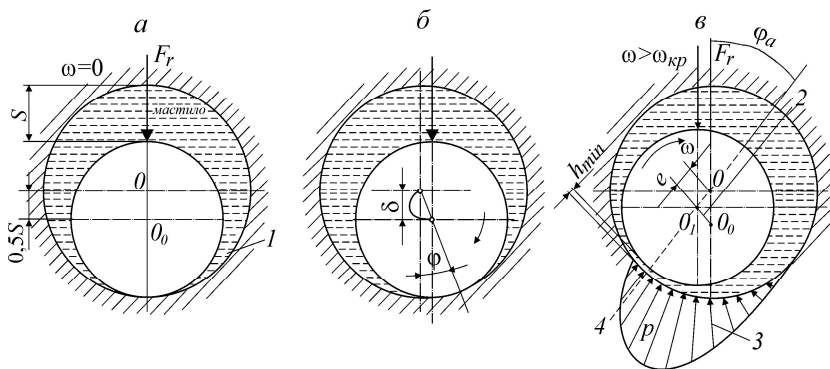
Положення вала в підшипнику й схема виникнення несучого мастильного шару:
